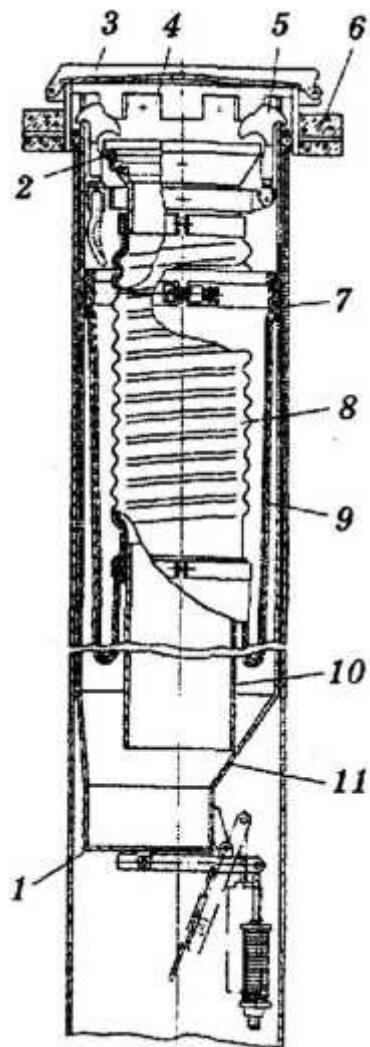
Установка нижнего слива СПГ-200: 1- обратный клапан с противовесом; 2 - уплотнительное кольцо; 3 - крышка; 4 - присоединительная головка; 5 - зажим; 6 - перекрытие сливного желоба; 7- обойма; 8- гофрированный рукав; 9- гибкий корпус; 10 - алюминиевый патрубок; 11 - сливная труба
